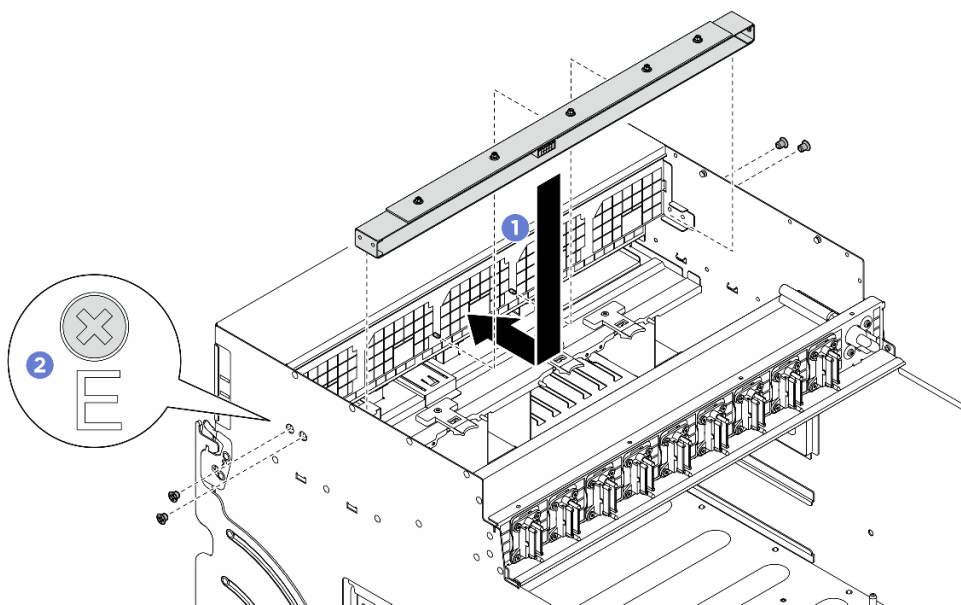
Instalação do conjunto de placa de controle do ventilador frontal
